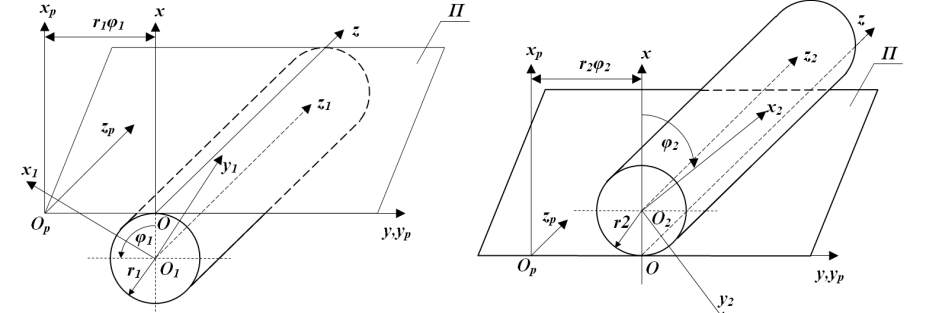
К образованию поверхностей зубьев зубчатых колёс
